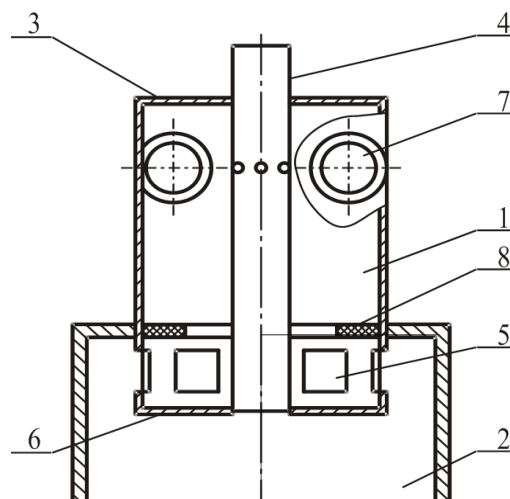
Конструктивная схема центробежно-вихревого деаэратора: 1 – корпус; 2 – центробежный сепаратор; 3 – верхняя торцевая крышка корпуса; 4 – трубопровод отвода пара; 5 – окна для отвода воды из корпуса; 6 – днище корпуса; 7 – подводные тангенциальные патрубки; 8 – кольцевая перегородка (шайба)
